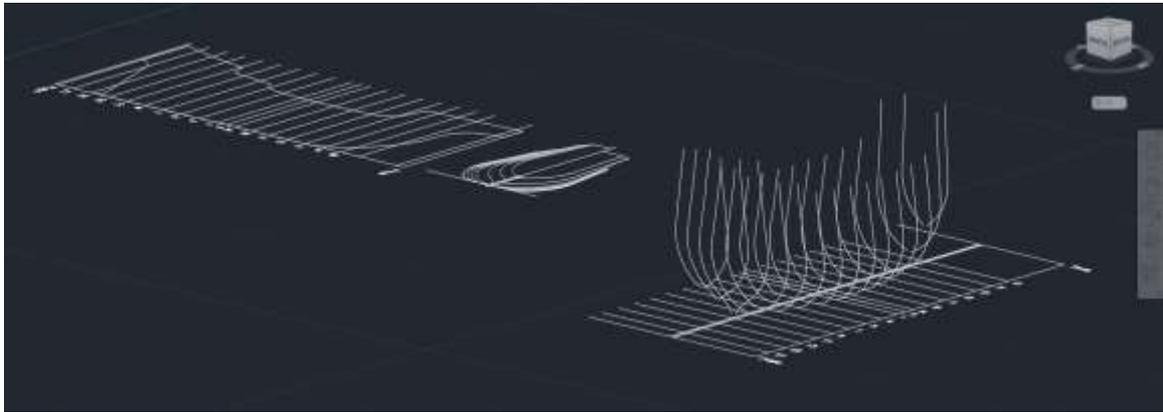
Vista isométrica de las secciones transversales del casco de la nao Santa María
